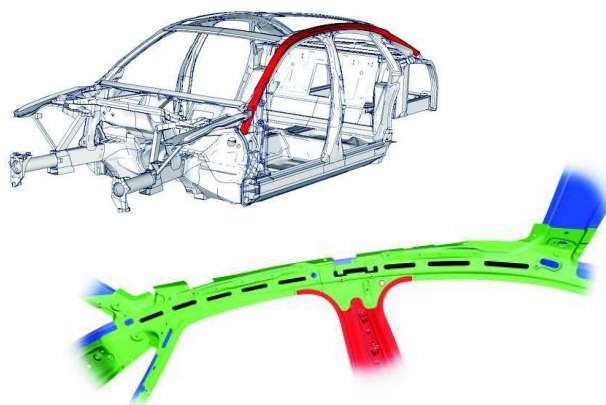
Schweißgruppe "Dachrahmen seitlich" der Aluminiumkarosserie des neuen Audi A8
